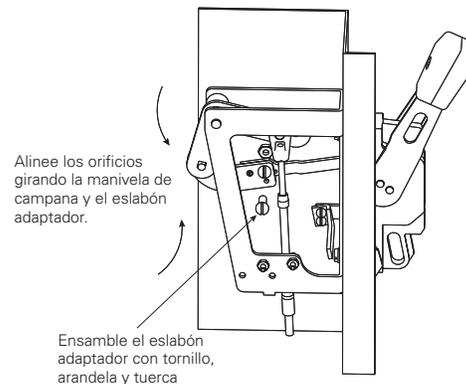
Ensamble de eslabón adaptador para eslabón actuador
